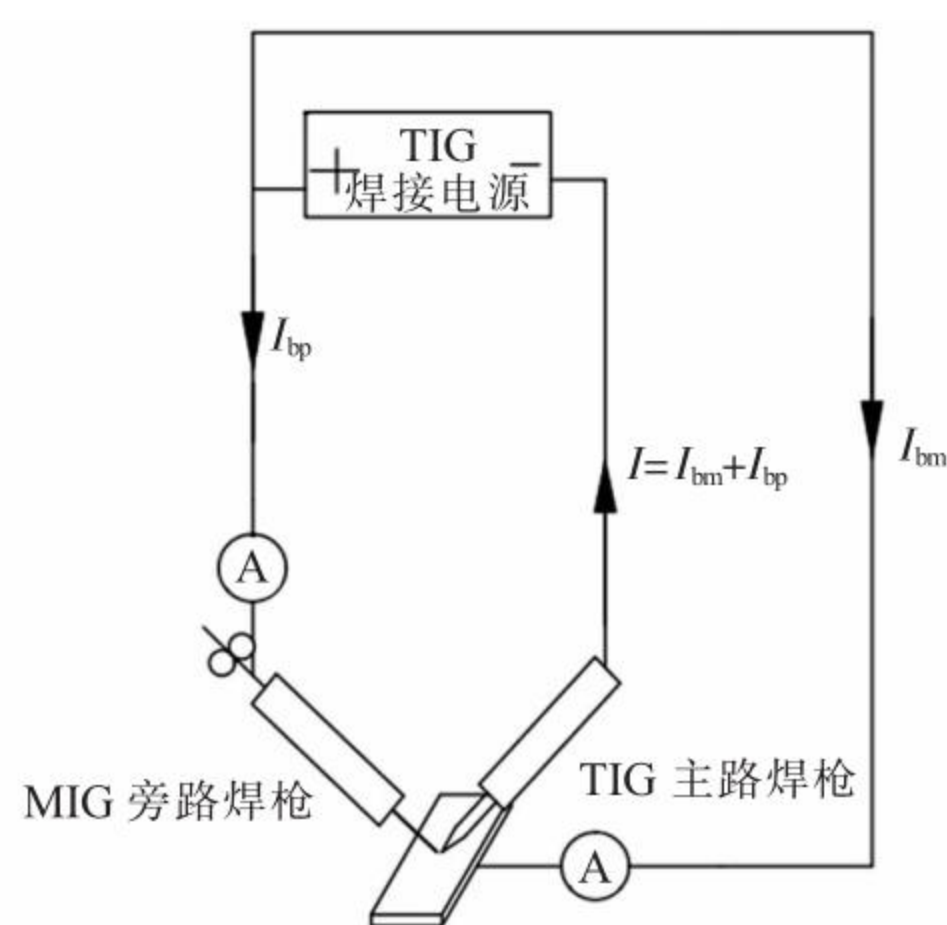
单电源旁路耦合电弧 TIG 焊原理图
